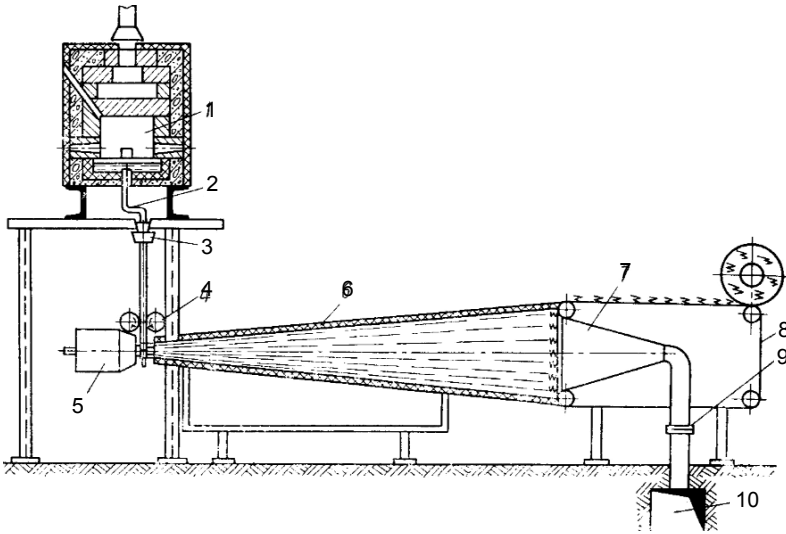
Технологічна схема виготовлення базальтового надтонкого волокна: 1 — ванна піч; 2 — струменевий живильник; 3 — фільтрна посудина; 4 — погумовані валки; 5 — камера згоряння; 6 — дворукавний дифузор; 7 — приєднувальний патрубок; 8 — сітка конвеєра; 9 — регулювальний шибєр; 10 — підземний канал
